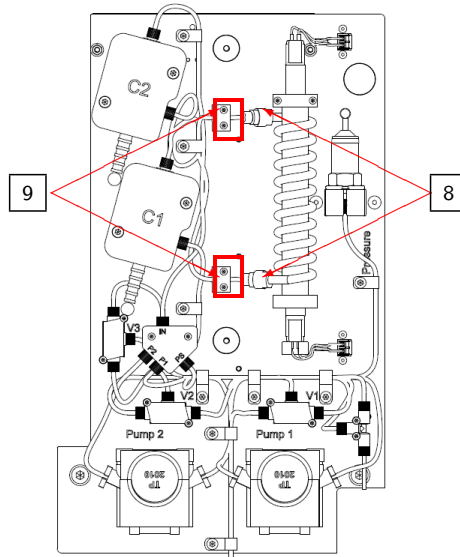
Fittings (8) an der Reaktor-Glaswendel verschrauben
